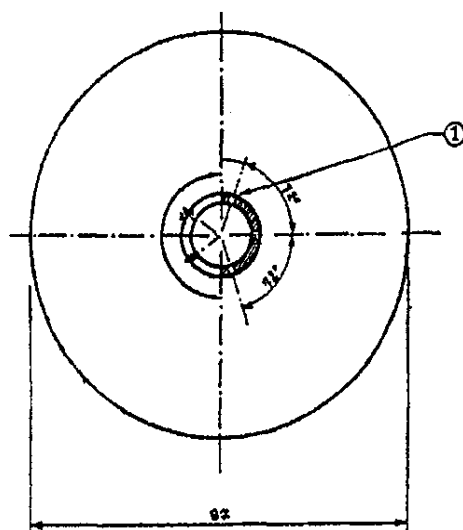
cilindro oco em bronze, fechado dum lado; plano e corte vertical em mm.
